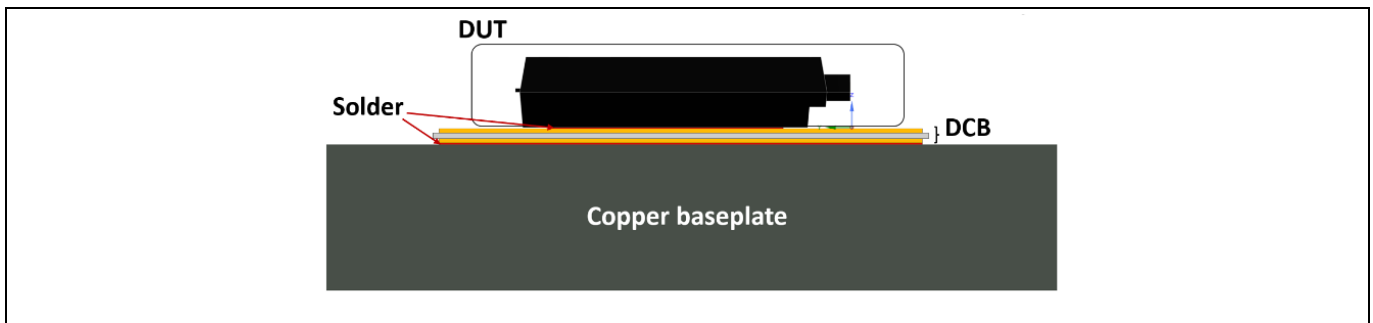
仿真系统 TO-247PLUS SMD 封装（DUT）焊接在 DCB 顶部，DCB 底部焊接在铜基板上
